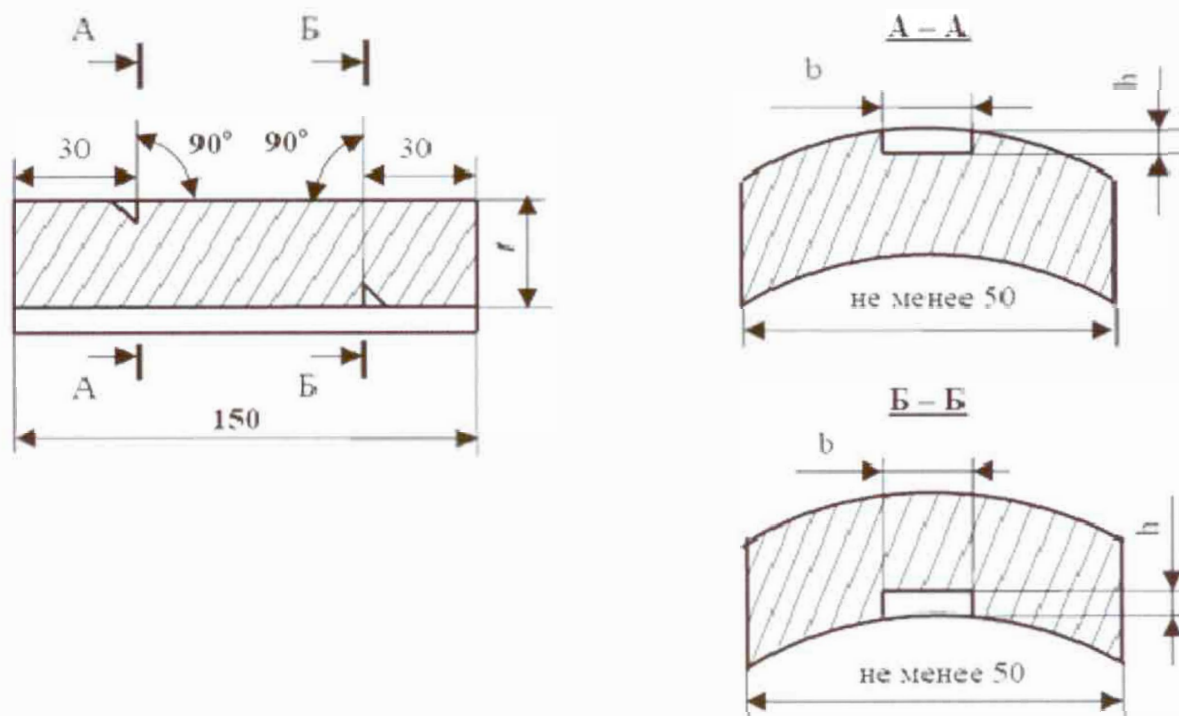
Чертеж СОП для настройки браковочного уровня
